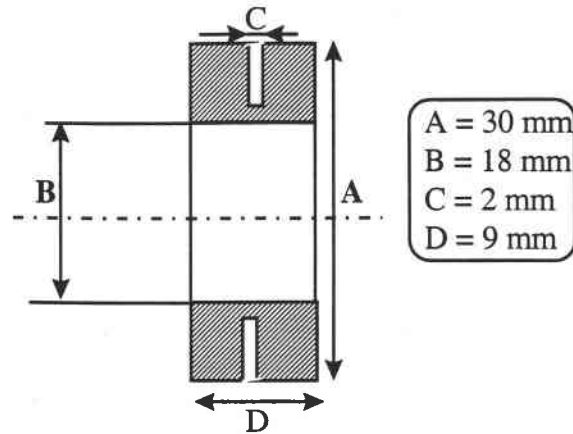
Géométrie de l'éprouvette de torsion [11].
